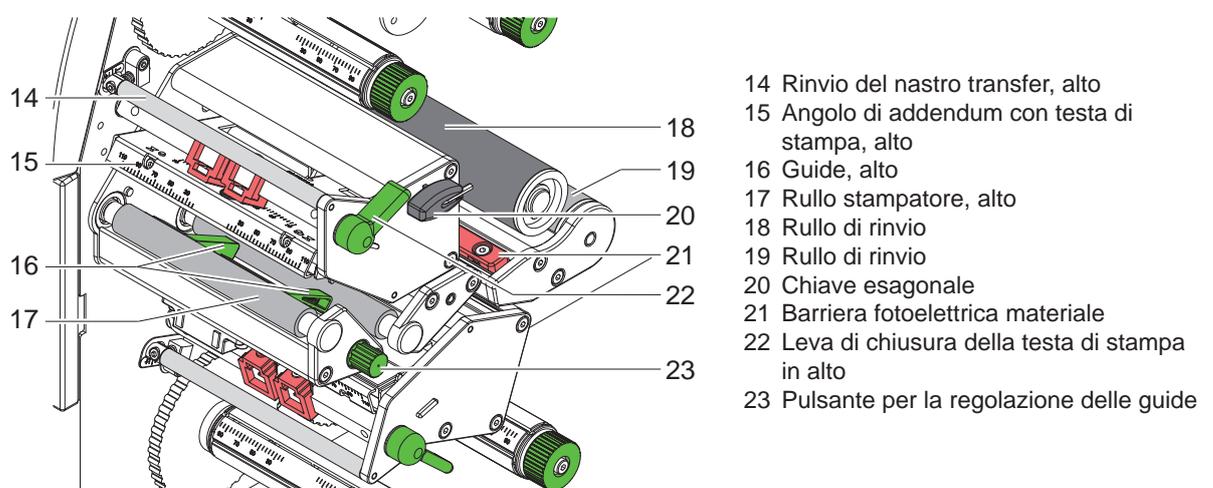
Meccanica di stampa - gruppo superiore stampante XD4M
